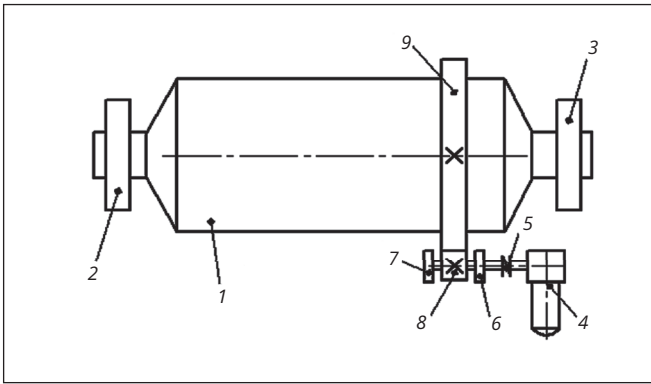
Кинематическая схема модернизированной мельницы МШЦ 2,1×3,0: 1 – барабан; 2 и 3 – подшипниковые опоры барабана; 4 – мотор-редуктор; 5 – муфта; 6 и 7 – подшипниковые опоры вала-шестерни; 8 – вал-шестерня; 9 – зубчатый венец
